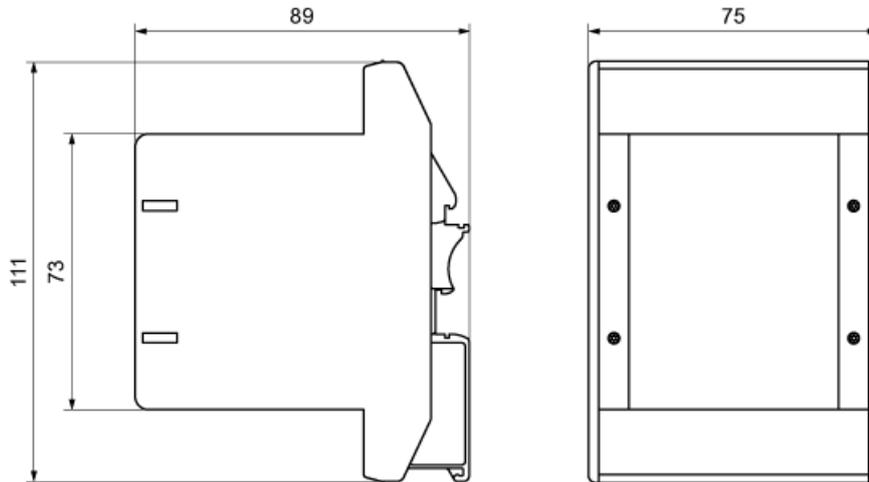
Maßbild Safe Brake Adapter (Angaben in mm)
